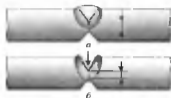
Приглушение кромки при двухсторонней сварке, недостаточное приглушение (нижний рисунок) вызывает сквозное проплавление и вытекание расплавленного металла. *а* — нормальное приглушение кромок, *б* — недостаточное приглушение кромок
